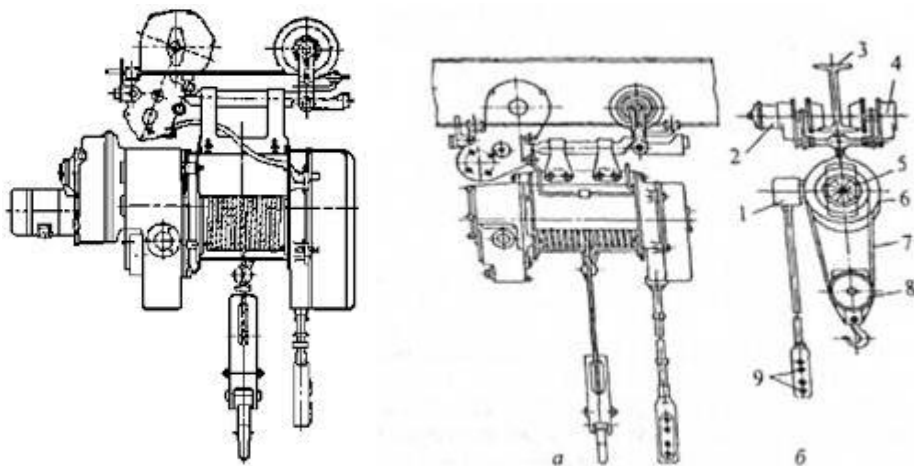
Електричний таль; а — зовнішній вигляд; б — схема: 1 — магнітний пускач; 2 — електродвигун для пересування; 3 — рейка; 4 — ходовий візок; 5 — електродвигун для підймання; 6 — корпус вантажного механізму; 7 — канат; 8 — підвіска; 9 — кнопки керування.
